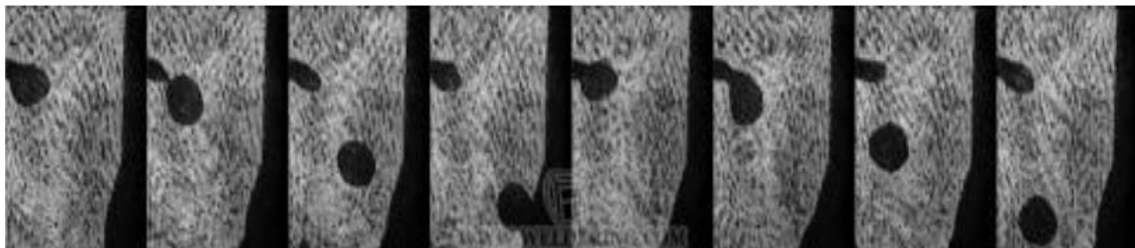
Втрати металу під час зварювання у вертикальному положенні
